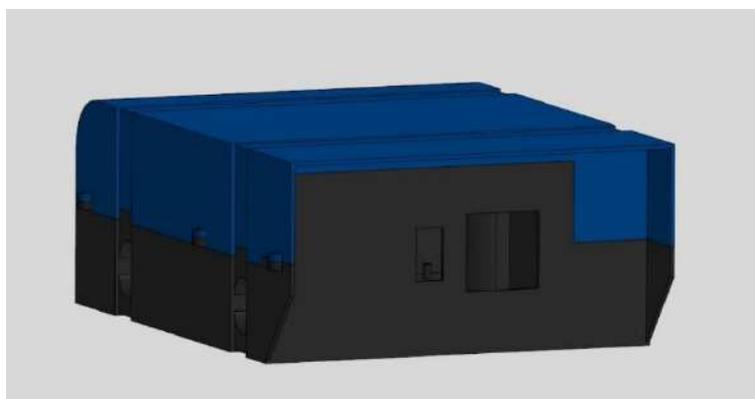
3D-модель защитного корпуса системы технического зрения
